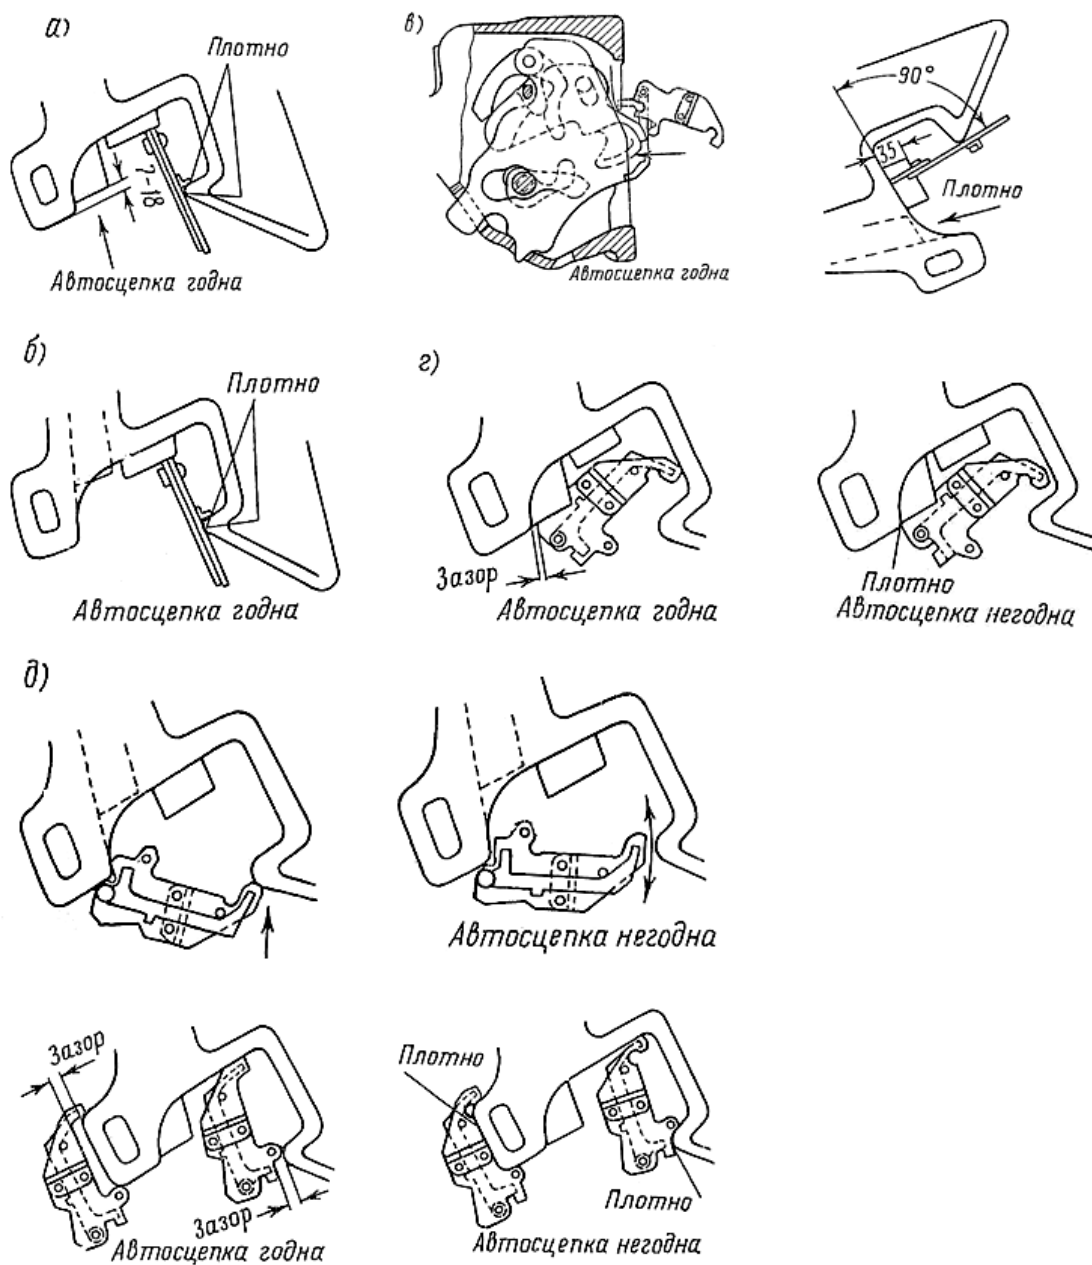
Проверка размеров и действий собранной автосцепки
